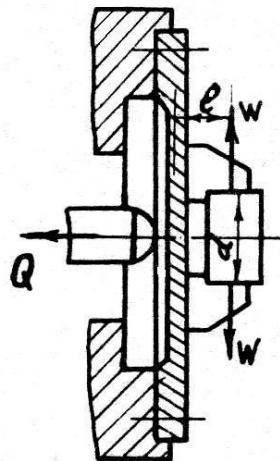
Схема установки і визначення зусилля затиску в мембранному патроні
